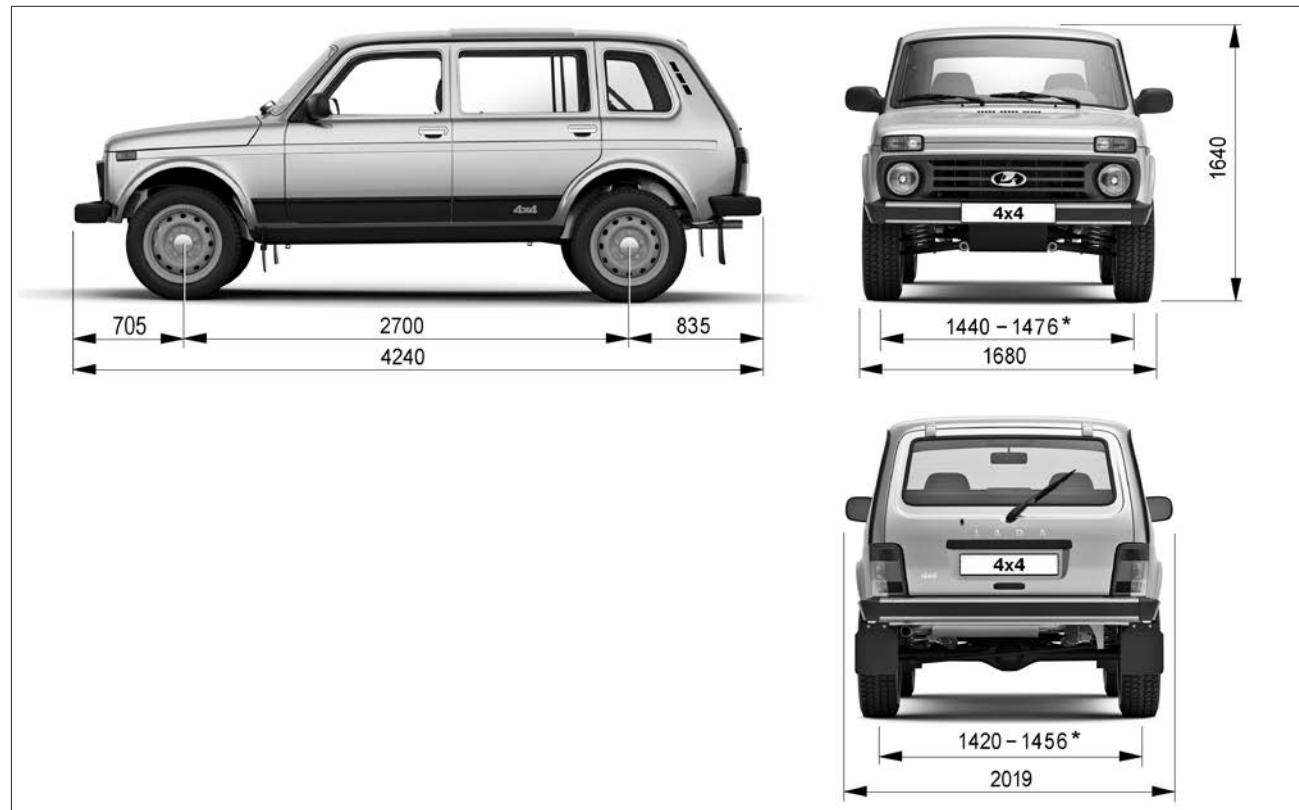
Габаритные размеры автомобиля LADA 4x4 5 дв.
